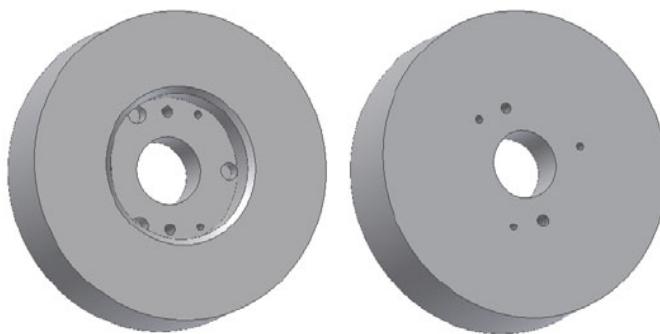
Součást pro uchycení zařízení SICK LMS 291 [2]
